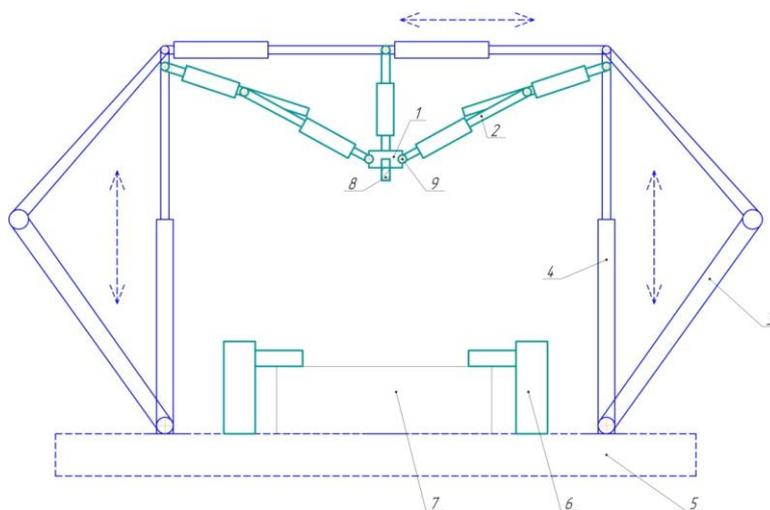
рама для обработки деталей типа «корпус подшипника».
